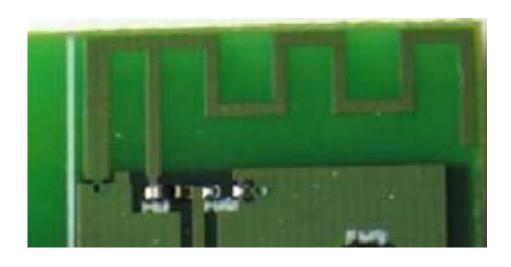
曲流型天线在 PCB 中制作成板载天线的应用示范
